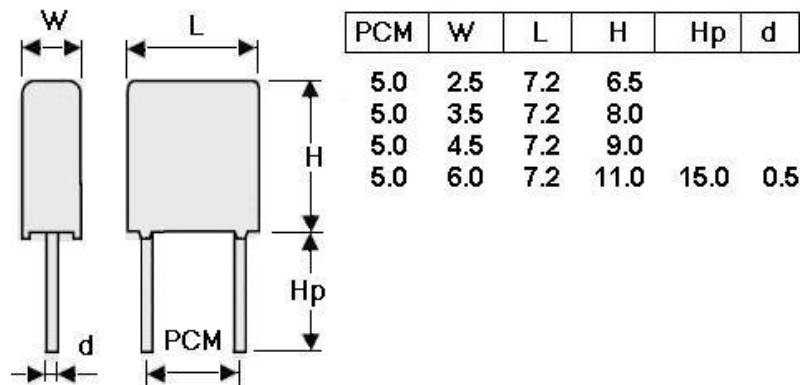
Габаритні розміри конденсатора B32529C1102J000
